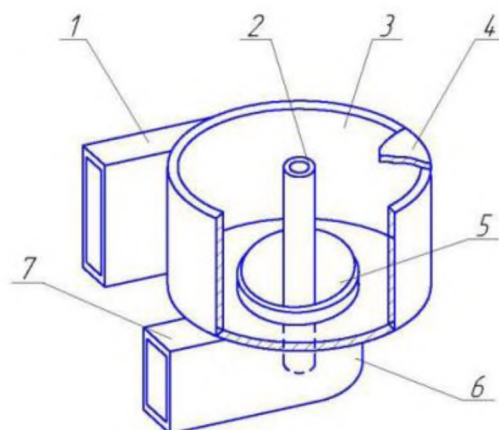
Вихрова сушарка :1 – вхідний патрубок; 2 – труба;
